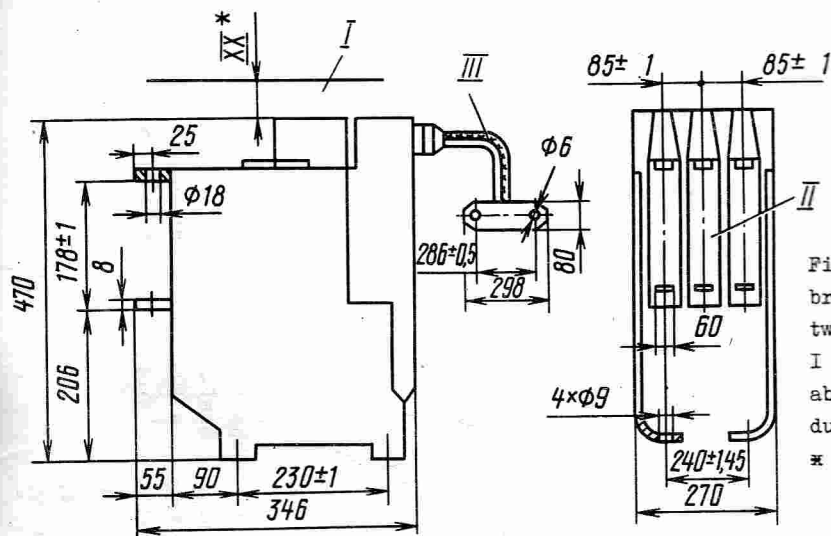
Габаритные и установочные размеры выключателей Э06С с электродвигательным приводом в двух- и трехполюсном исполнении:
